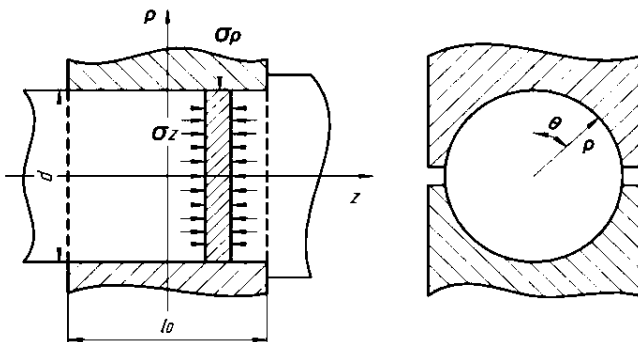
Схема протяжки заготовки круглого сечения в вырезных бойках
